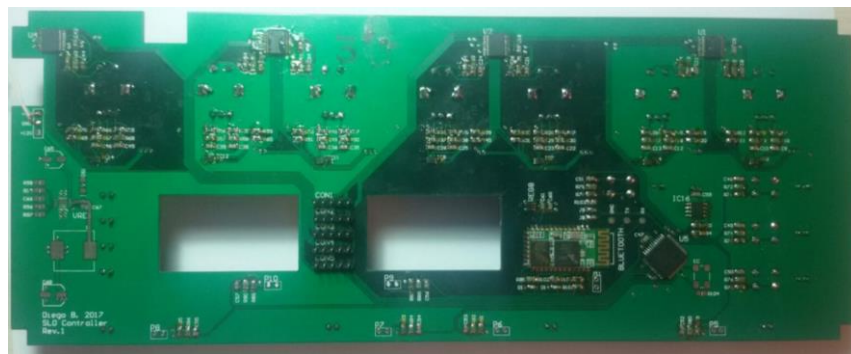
“Vista cara Bottom de la pcb del footswitch con los componentes”
